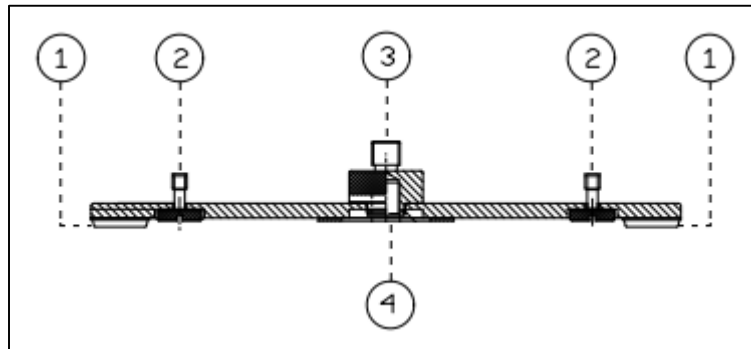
Staffa di supporto BVA325 – Vista frontale.
